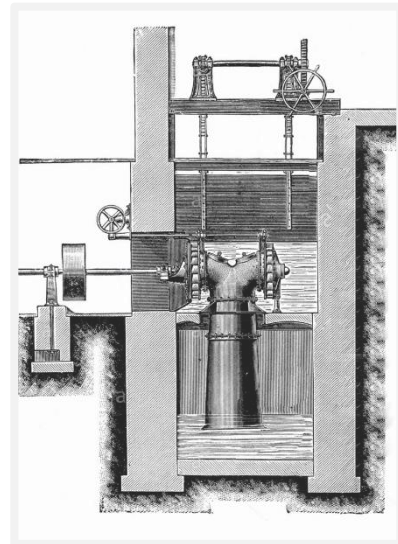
Desenho em corte da Turbina (desenho retirado de www.alamy.com)
